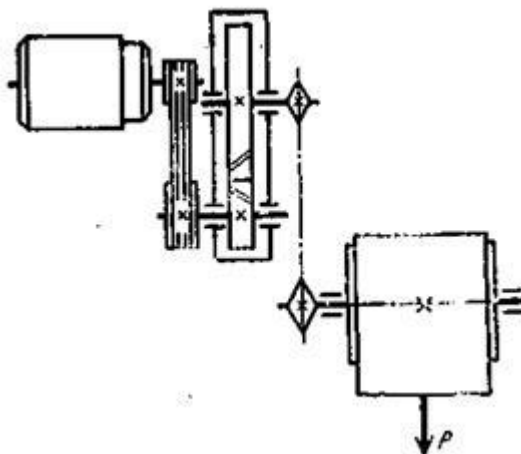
Кинематическая схема привода ленточного транспортера
